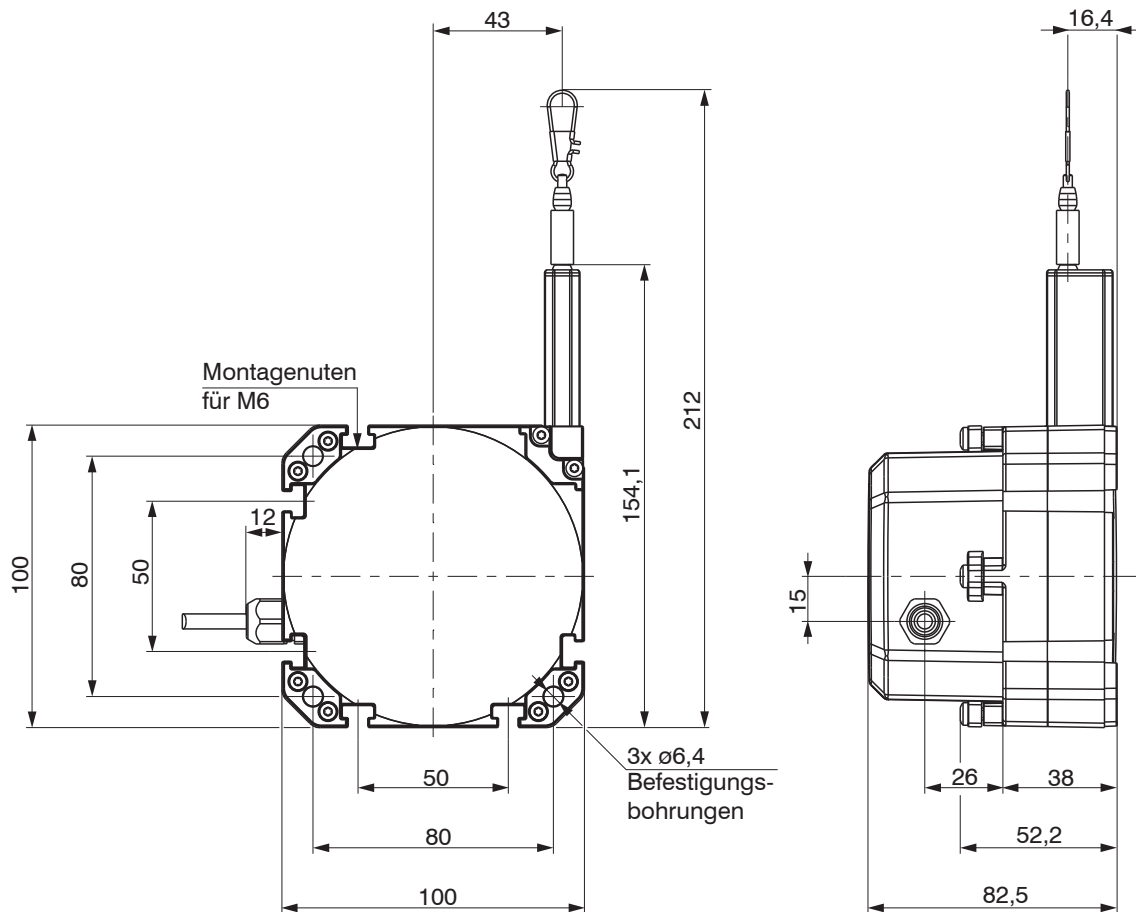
Maßzeichnung WPS-3500-K100, WPS-5000-K100, Abmessungen in mm, nicht maßstabgetreu
